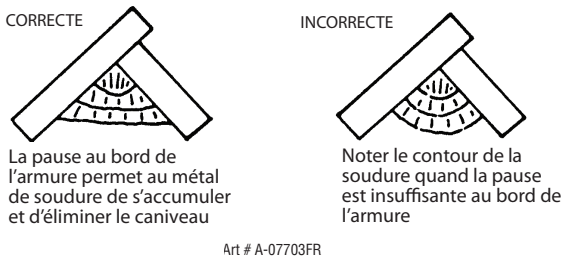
Exemples de soudure d'angle Verticale
